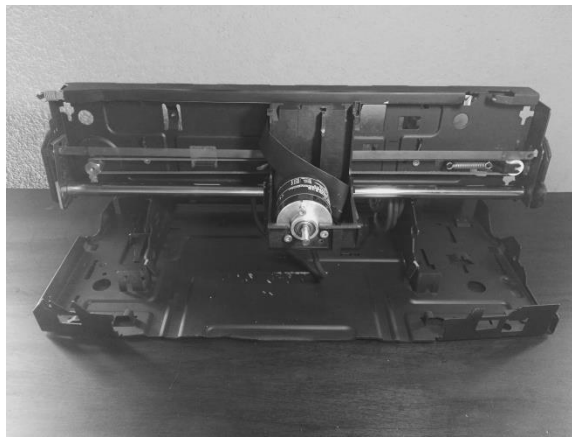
Vista anterior del marco de la impresora con codificador del péndulo y motor de engranajes de cc ensamblados.
